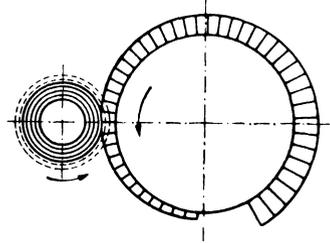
Außenrundräumen mit fortlaufender Werkzeugbewegung (Werkstück außerhalb der Werkzeugkreisbewegung).
